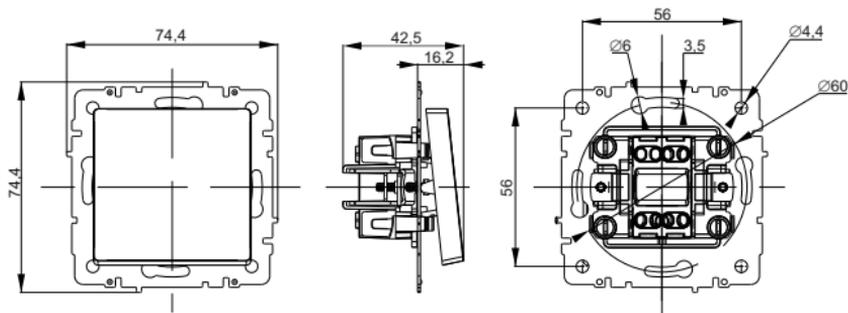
Габаритные и установочные размеры выключателей без рамки / Figure 2 – Overall and mounting dimensions of switches without frame / 2-сурет – Жақтауы жоқ ажыратқыштардың габаритті және орнату өлшемдері / Рисунок 2 – Габаритні та установчі розміри вимикачів без рамки / Attēls 2 – Bezrāmja slēdžu gabarīta un uzstādīšanas izmēri / Pav. 2 – Jungkliķi īsmatavimai ir montavimo dydžiai be rėmelio / Joonis 2 – Raamita lülitite üld-ja paigaldusmõõtmed / Figura 2 – Dimensiunile și dimensiunile de instalarea a comutatoarelor fără cadru / Bild 2 – Haupt- und Anschlussabmessungen der Schalter ohne ein Rähmchen
